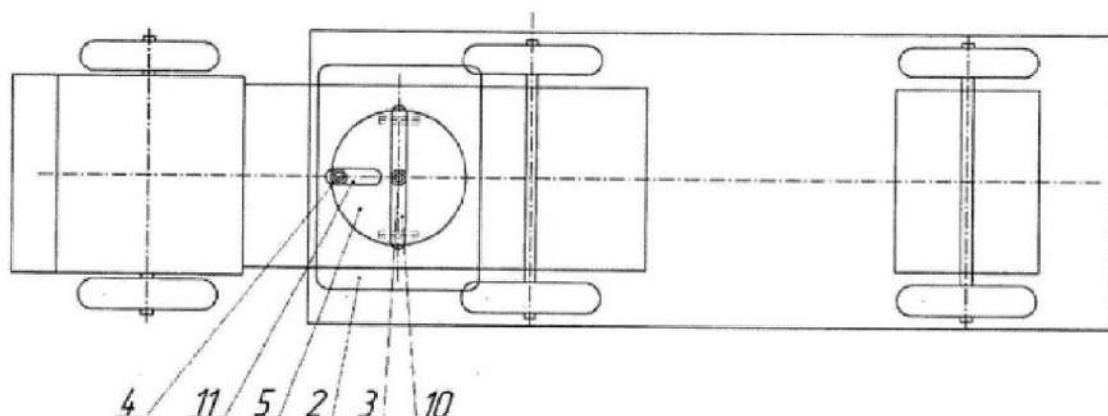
Схема опорно-поворотного пристрою автопоїзда
